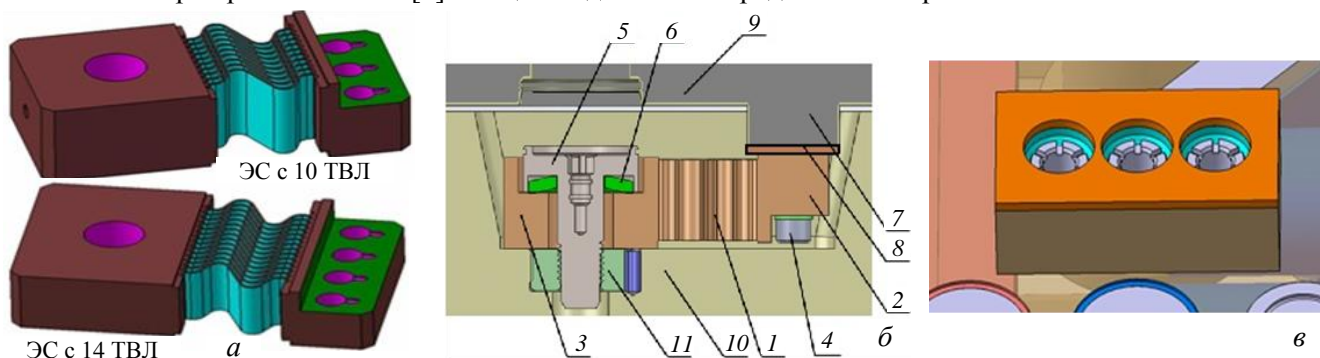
Общий вид ЭС ППС (а); схема ЭС ППС (б): 1 — ЭС, 2 — боковой фланец ЭС, 3 — центральный фланец ЭС, 4 — винт М12, 5 — винт М24, 6 — тарельчатая пружина, 7 — стальной пьедестал, 8 — слой бронзы CuCrZr , 9 — НКПС, 10 — ЗБ, 11 — резьбовая втулка ЗБ; в — вид на биметаллический пьедестал ЭС
